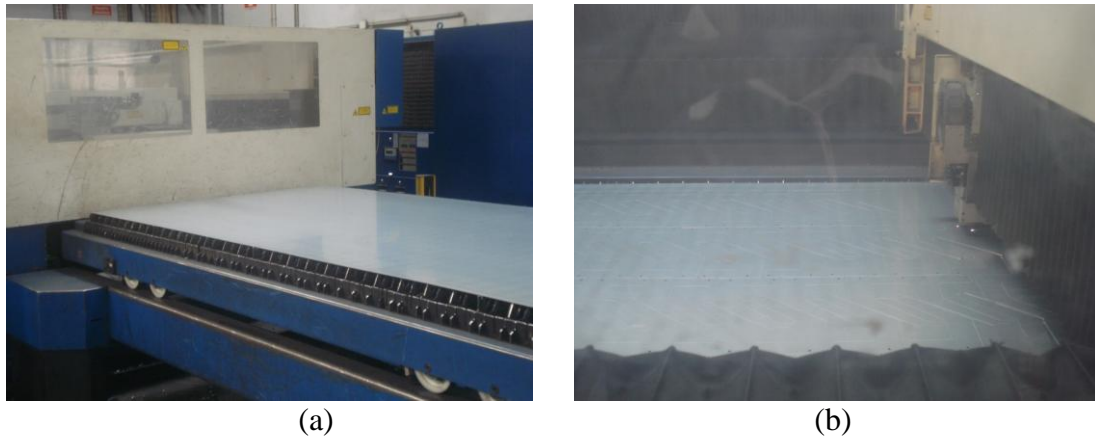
(a) Chapa nova na posição de corte; (b) Corte a laser em execução
